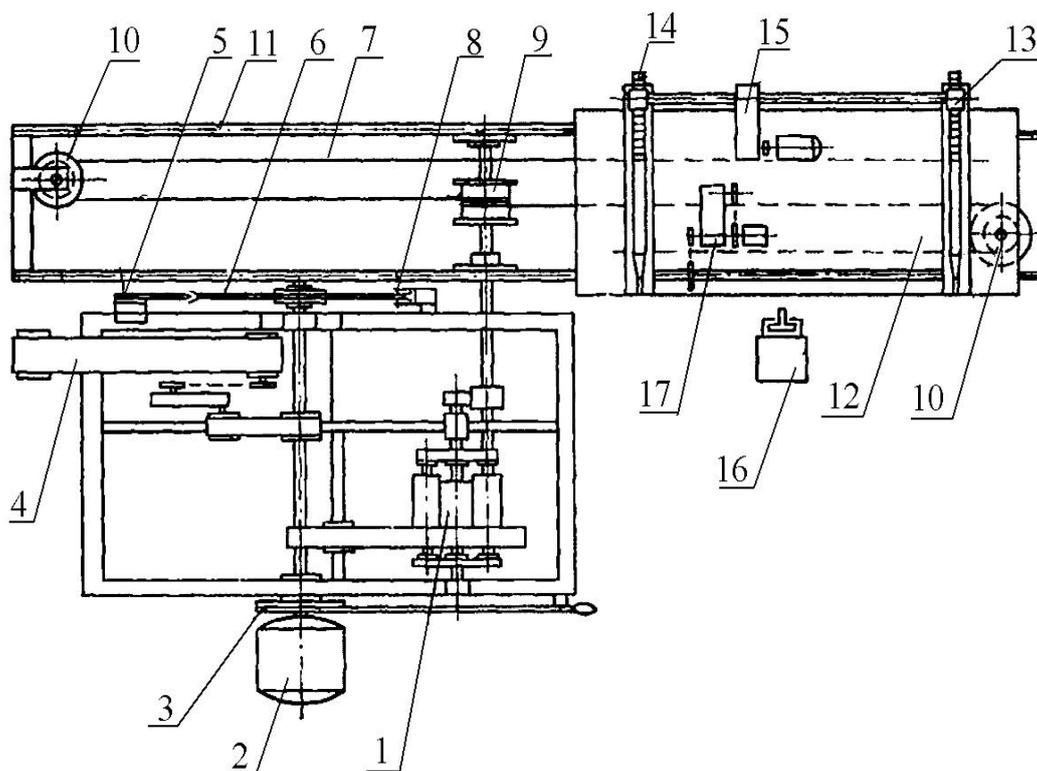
Схема шпалорезного станка ЦДТ-6-2
